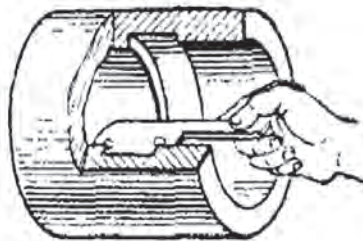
Вимірювання ширини внутрішньої канавки шаблоном
